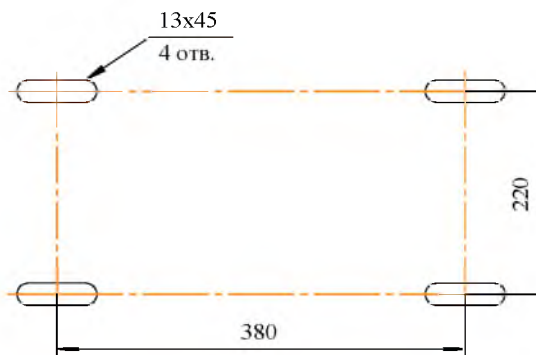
Расположение отверстий для крепления разъединителя
